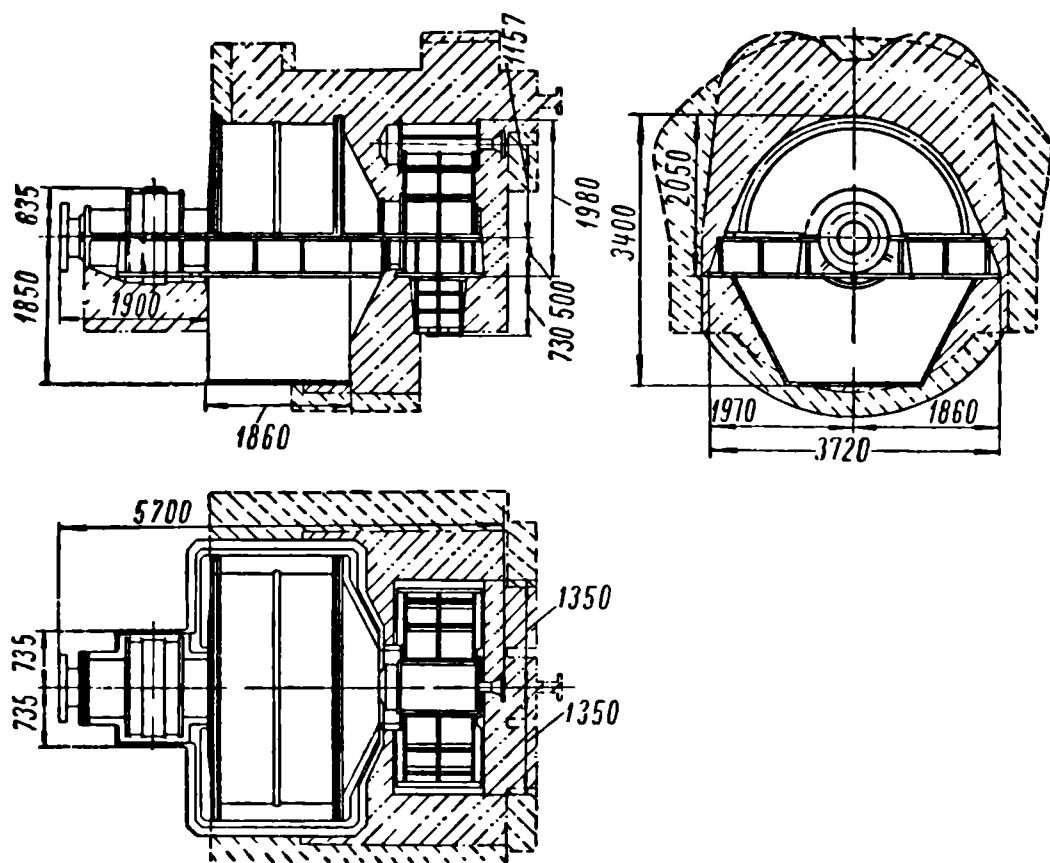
Сравнение габаритов реверсивного планетарного редуктора (рис. 2), нереверсивного двухступенчатого редуктора (силуэт — штрих-пунктирными линиями) и реверсивного непланетарного двухступенчатого редуктора (силуэт — штриховыми линиями).
